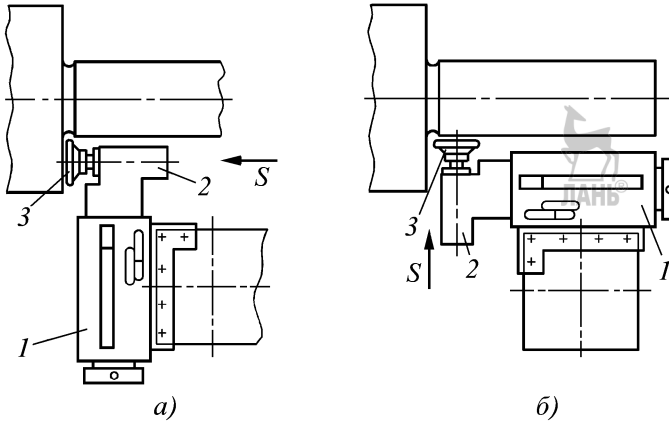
Схемы обкатывания поверхностей на токарных станках посредством однороликовых приспособлений:
